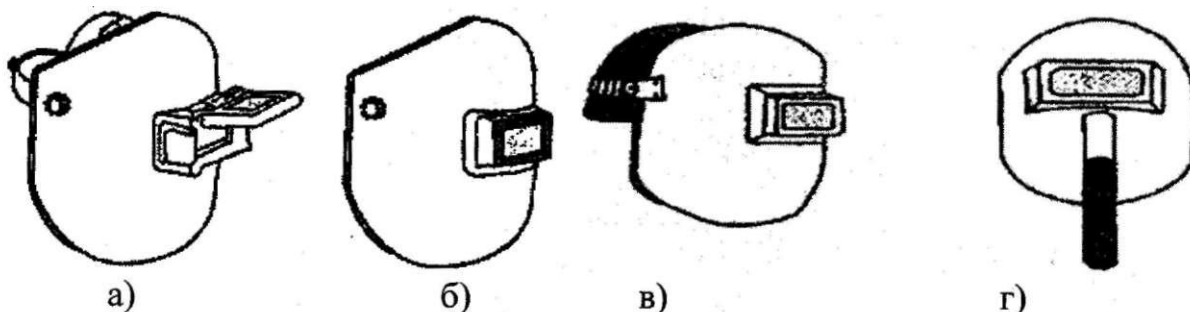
Наголовные щитки для сварочных работ
